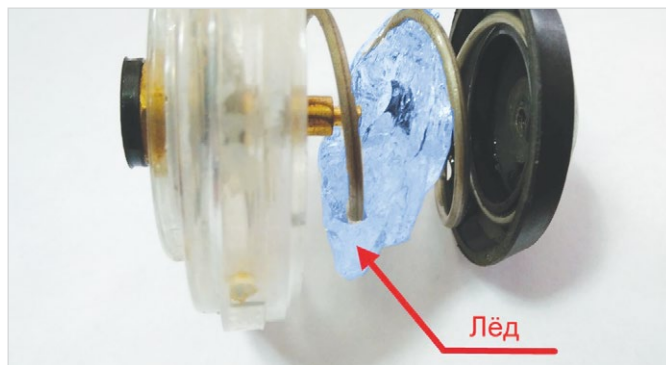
Большой кусок льда на пружине редуктора регулятора
